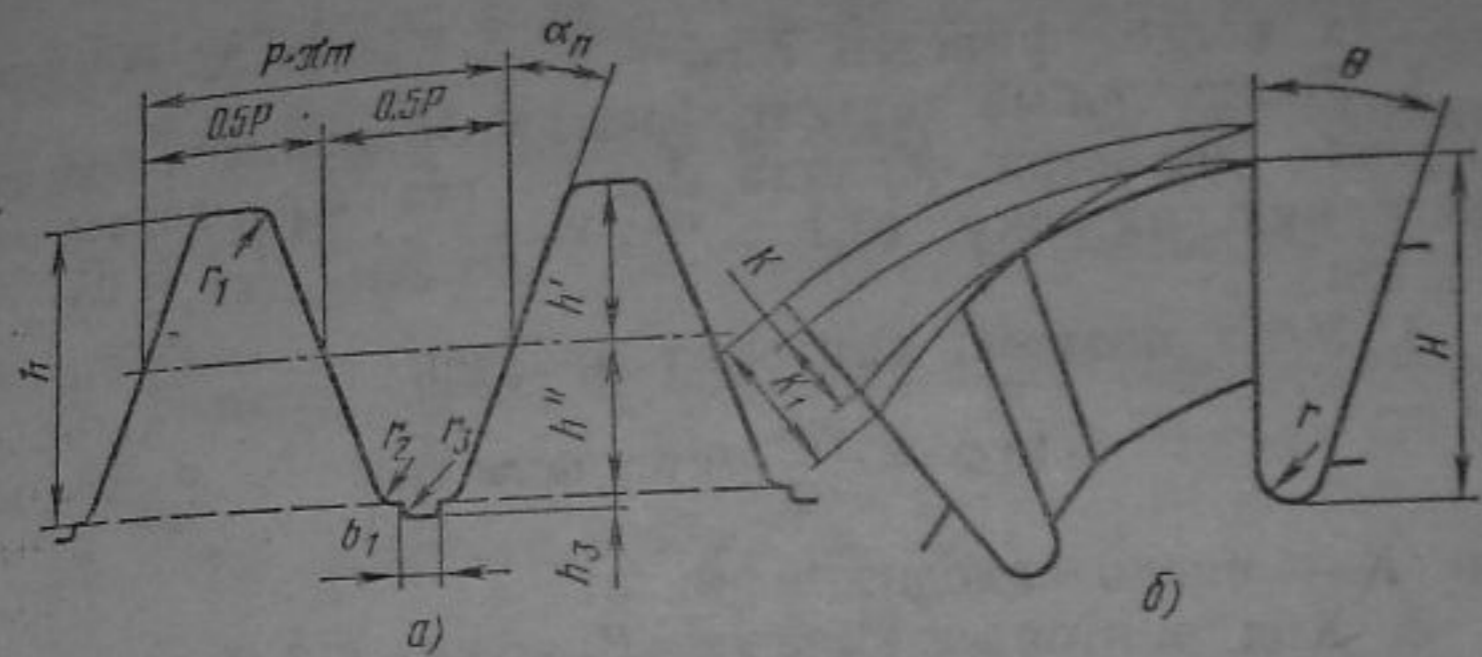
Схемы для определения элементов профиля (а) и затылования зубьев (б) червячной фрезы
